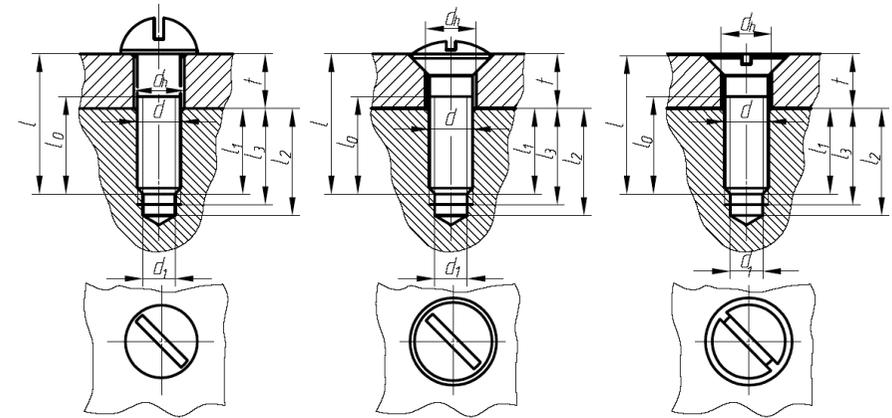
Конструктивные элементы и размеры деталей в соединениях винтами
